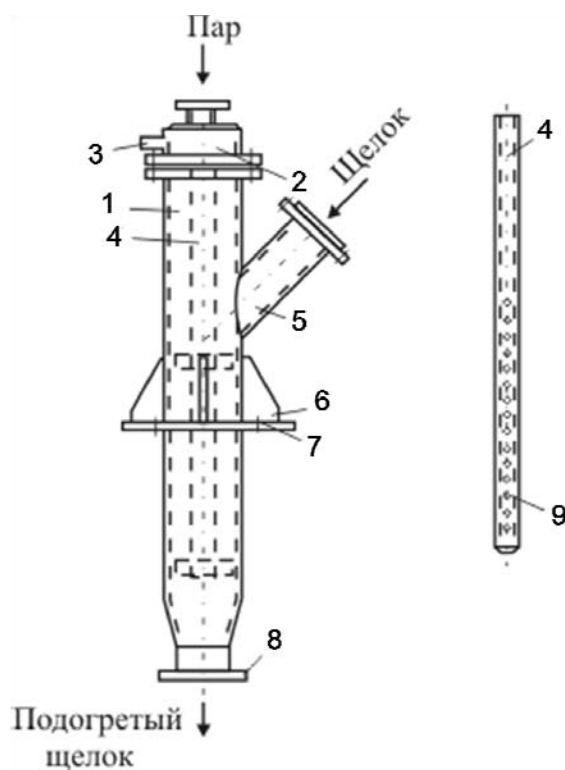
Общий вид и детали подогревателя смешивающего типа:
